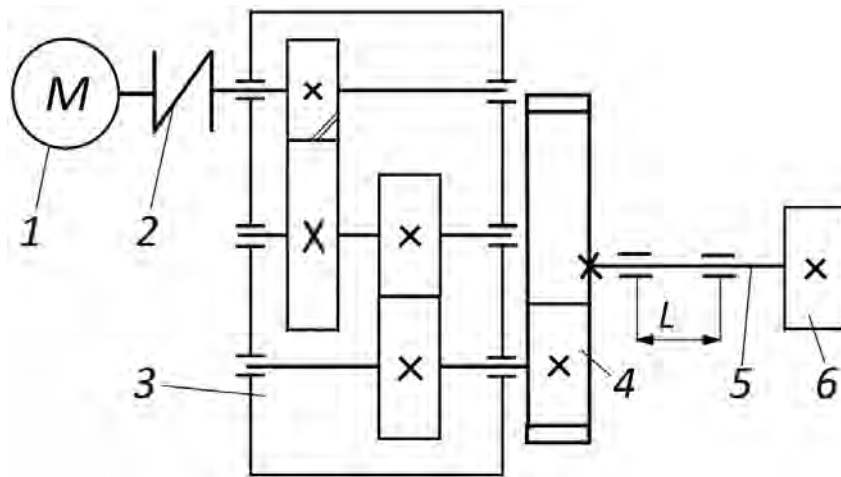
Схема привода поворотного устройства (вид сверху): 1 – асинхронный электродвигатель; 2 – муфта упругая с резиновой звездочкой; 3 – редуктор двухступенчатый (первая ступень – цилиндрическая косозубая зубчатая передача, вторая – цилиндрическая прямозубая зубчатая передача); 4 – открытая прямозубая цилиндрическая передача с внутренним зацеплением; 5 – приводной вал; 6 – прямозубая шестерня приводного вала
